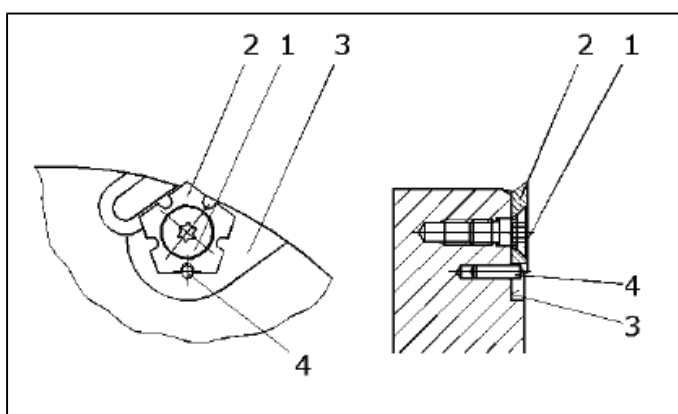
Upínací systém univerzálních nožů firmy Vydona [5].
